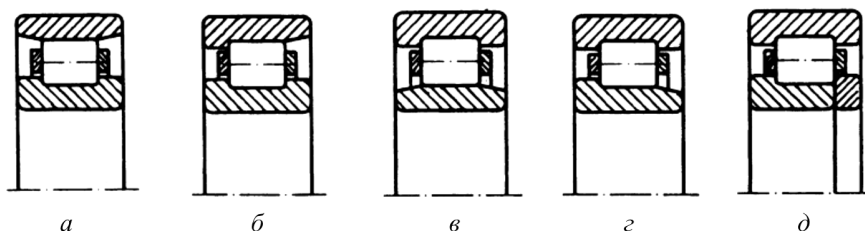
Роликовые радиальные подшипники с короткими цилиндрическими роликами
